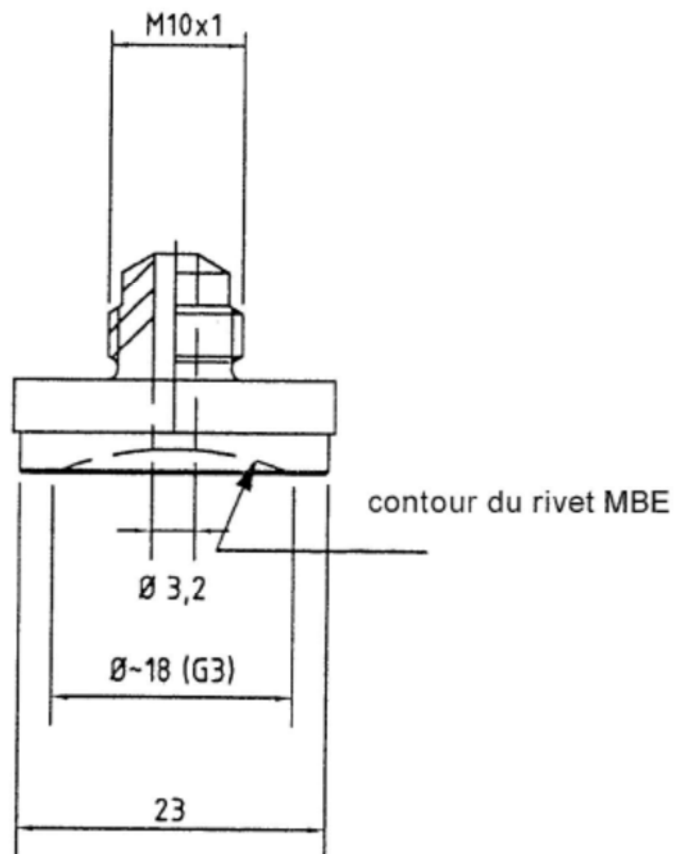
bis – Cale de serrage pour fixation des points coulissants
